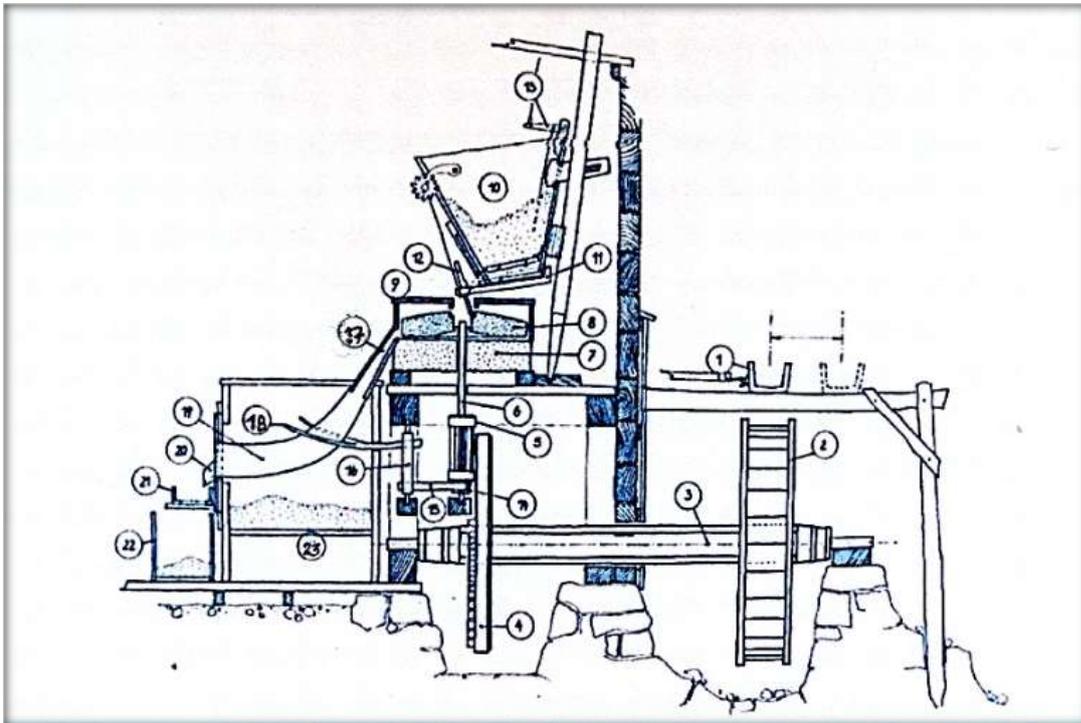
Funktionsschema einer Bauernmühle mit nur einem Mahlwerk. Quelle: Schema der Unterdiehmühle in Pfarrwerfen (rekonstruiert durch Alois Brandner, d.d. Verf.ergänzt).
